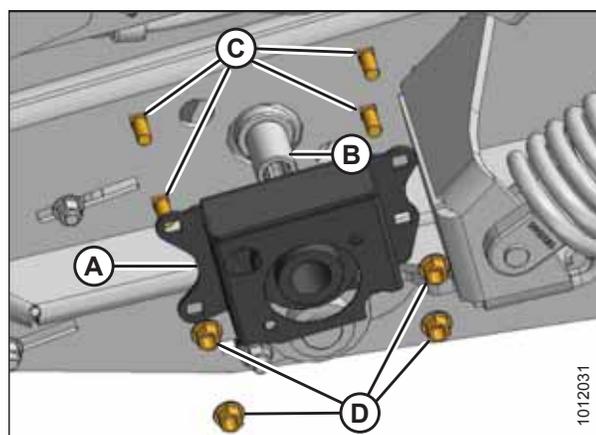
Soporte de motor con el nuevo rodamiento instalado
